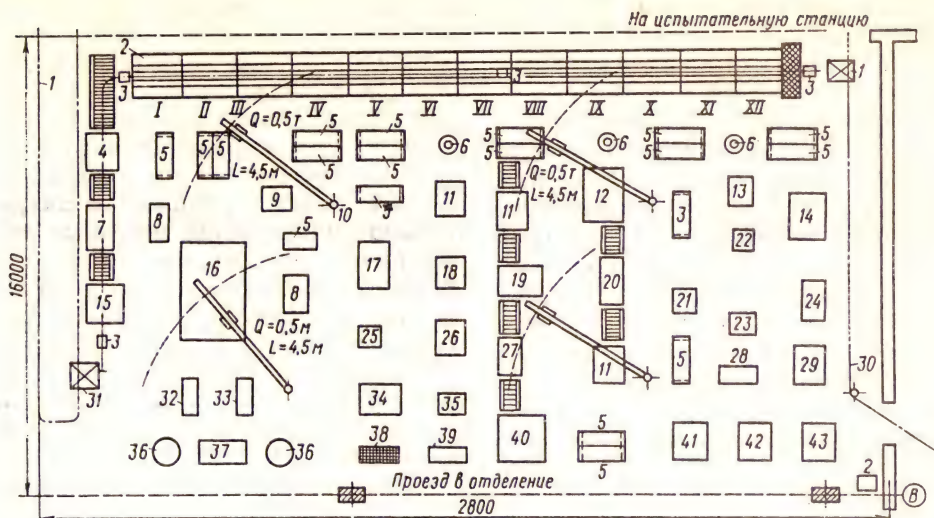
Планировка участка сборки двигателей авторемонтного завода с годовой программой 25 000 КР силовых агрегатов ГАЗ-53А:
